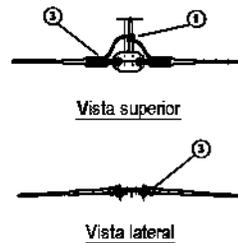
CONJUNTO DE TENSIÓN PARA CABLE DE GUARDA
